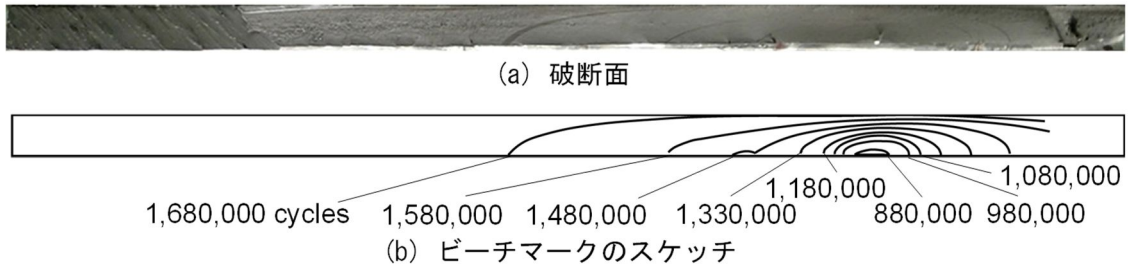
疲労試験後の破断面と、ビーチマークのスケッチ
